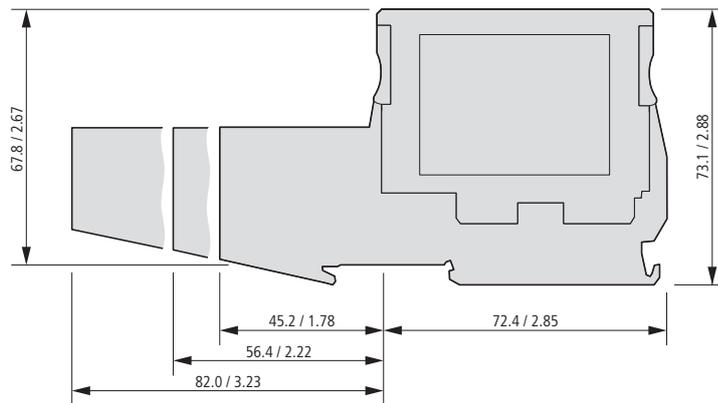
Seitenansicht BL20-Modul komplett (mit Zugfederanschluss)
